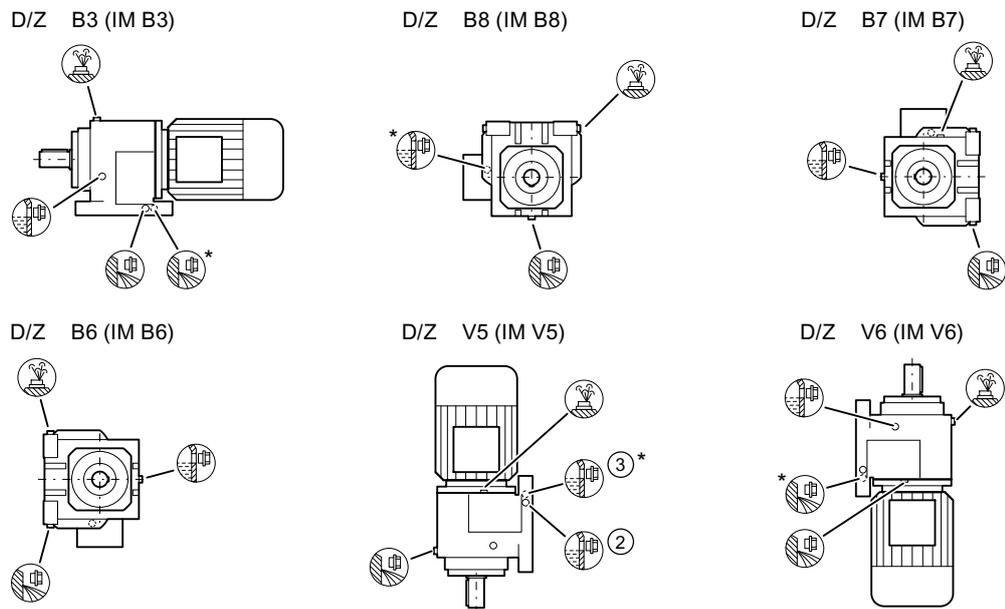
Formes de construction pour D/Z, tailles 108 - 168
